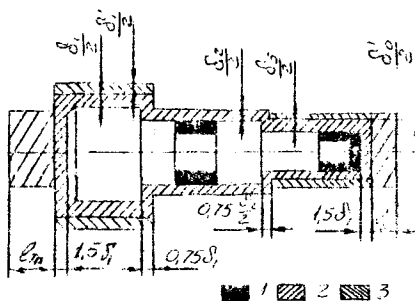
Эскиз детали с напусками (1), основными (2) и дополнительными (3) припусками
